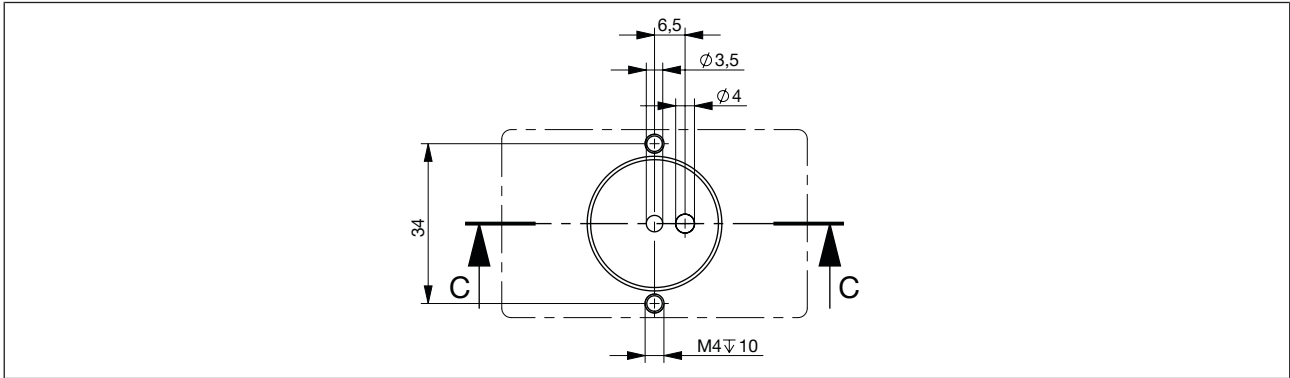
Anschlussbild 2 Einsteckflansch-Variante FC22
